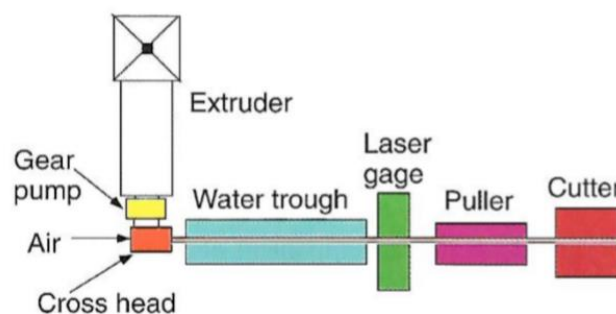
34 Componentes de línea de extrusión de tubos típica
